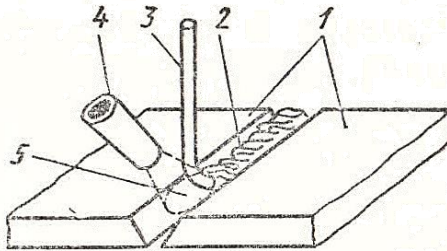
Газове зварювання з присадковим матеріалом:
